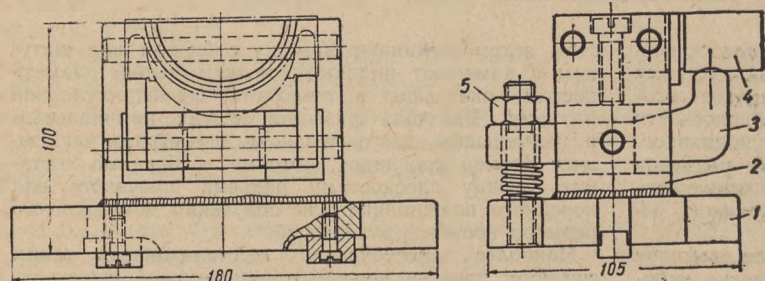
Приспособление для шлифования плоскости разъема крышек шатунов двигателя автомобиля ГАЗ-51:
